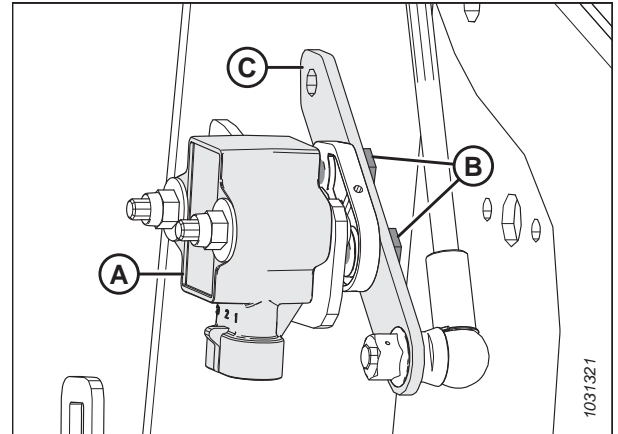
Haspelhöhsensor – Rechter Haspelarm
